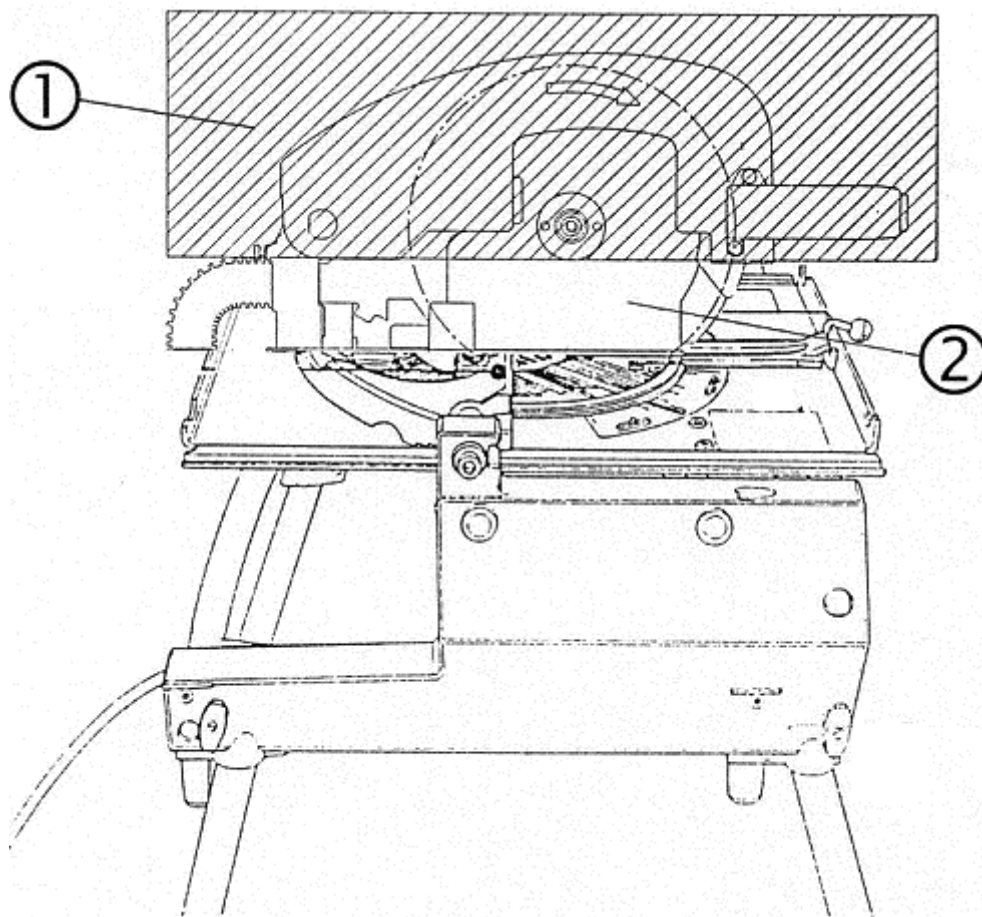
Kombinovaná pokosová pila-stolová kotoučová pila (typ B)
